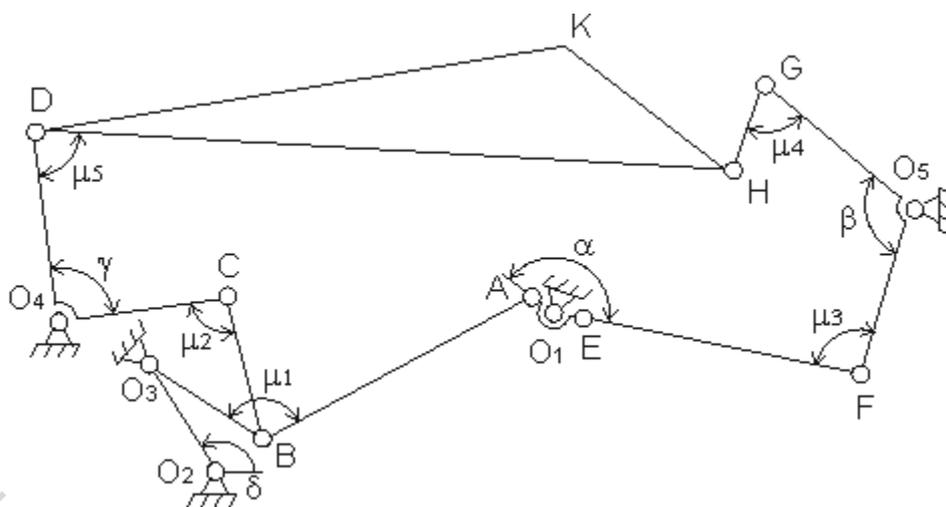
Кинематическая схема однореечного механизма продвижения материала универсальной швейной машины
